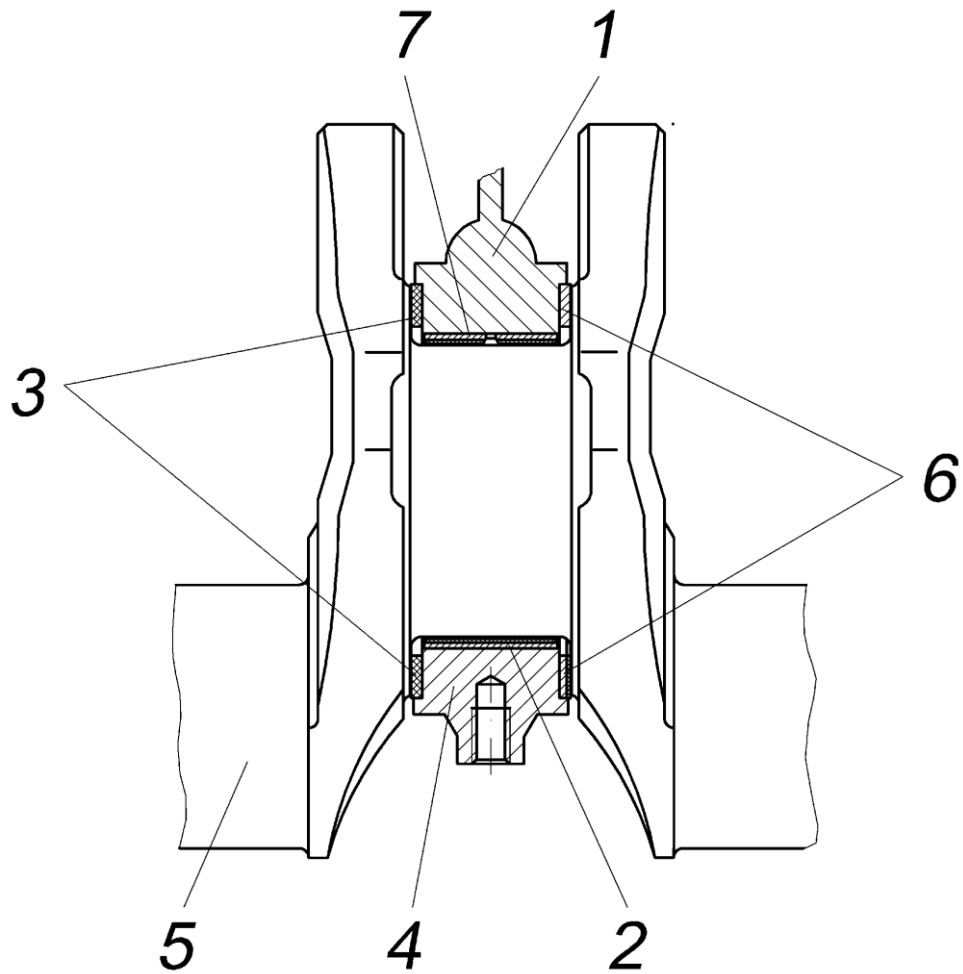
Средний (упорный) подшипник коленчатого вала
